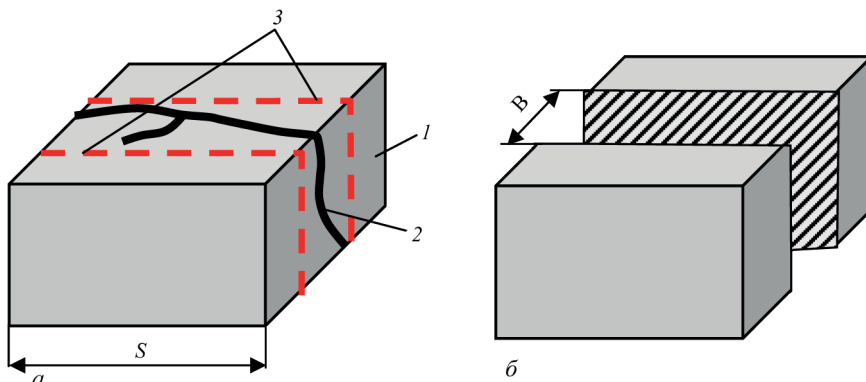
Схема розмітки (а) і видалення дефектного металу в районі наскрізної тріщини (б): 1 – деталь, що підлягає ремонту; 2 – наскрізна тріщина; 3 – площина розрізу; B – зварювальний проміжок
